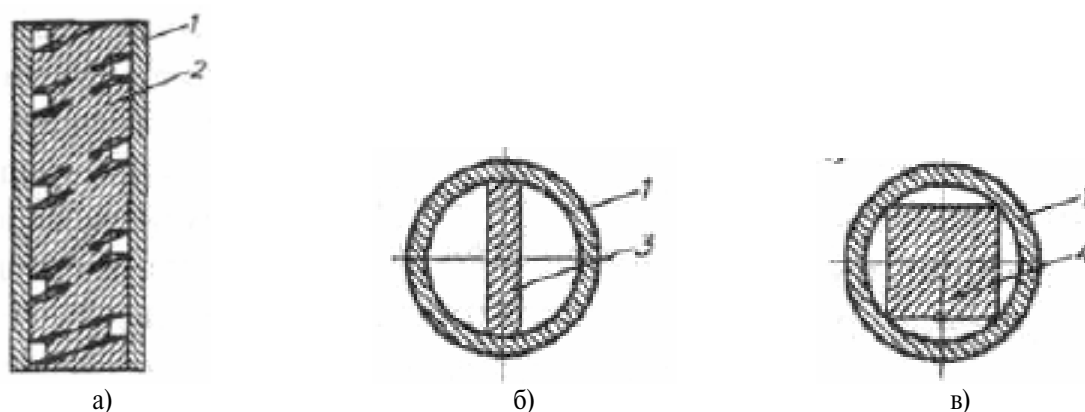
Конструкции трубчатых электродов-инструментов при прошивании особо глубоких отверстий: а – с нарезанным спиральным каналом; б – с пластиной; в – со стержнем квадратного сечения; 1 – трубка; 2 – деталь со спиральными канавками; 3 – пластина; 4 – квадратный стержень
